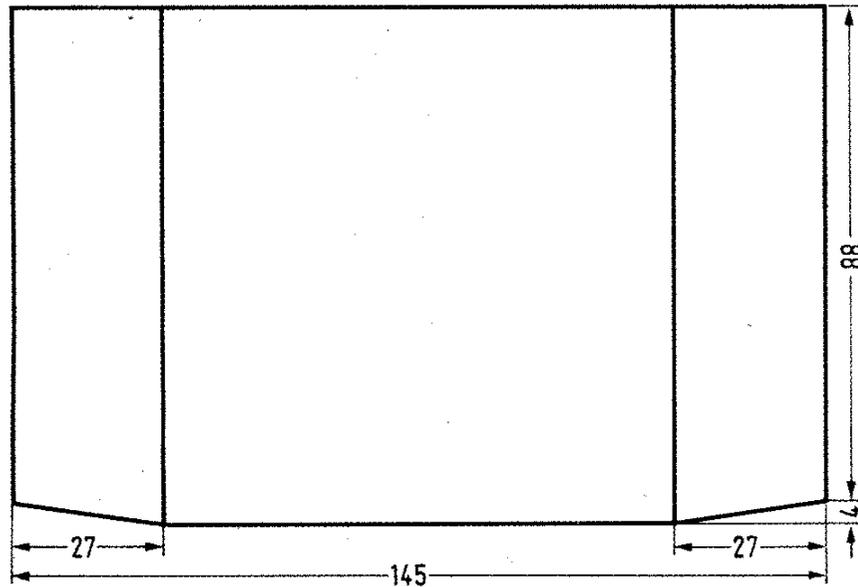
Maßangaben für das Gehäuse des Mustergerätes (in mm)
